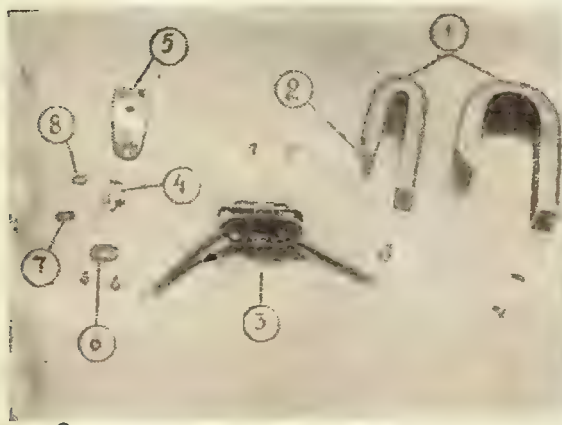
Детали рекордера т. Успенского: 1 — магниты индуктора (цифрой 2 показана выемка для крепления детали 3); 2—модуляционная часть с полюсными наконечниками; 3—якорь; 4 — планка крепления якоря; 5 — шайба крепления якоря; 6 — демфирующее кольцо
